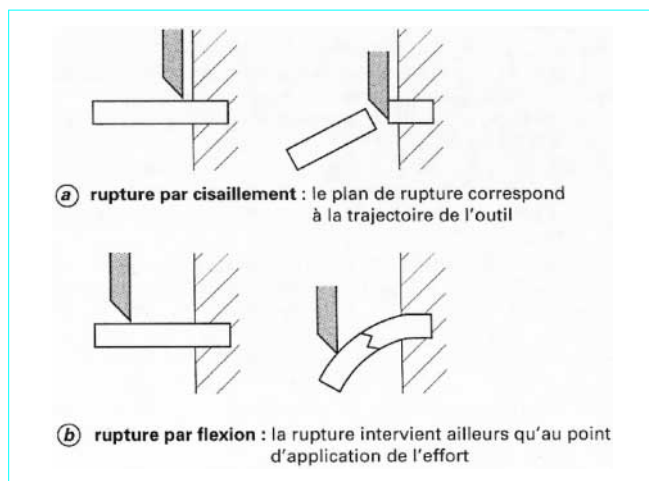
Principe de la formation du copeau en profilage en bout (mode 90-90)
